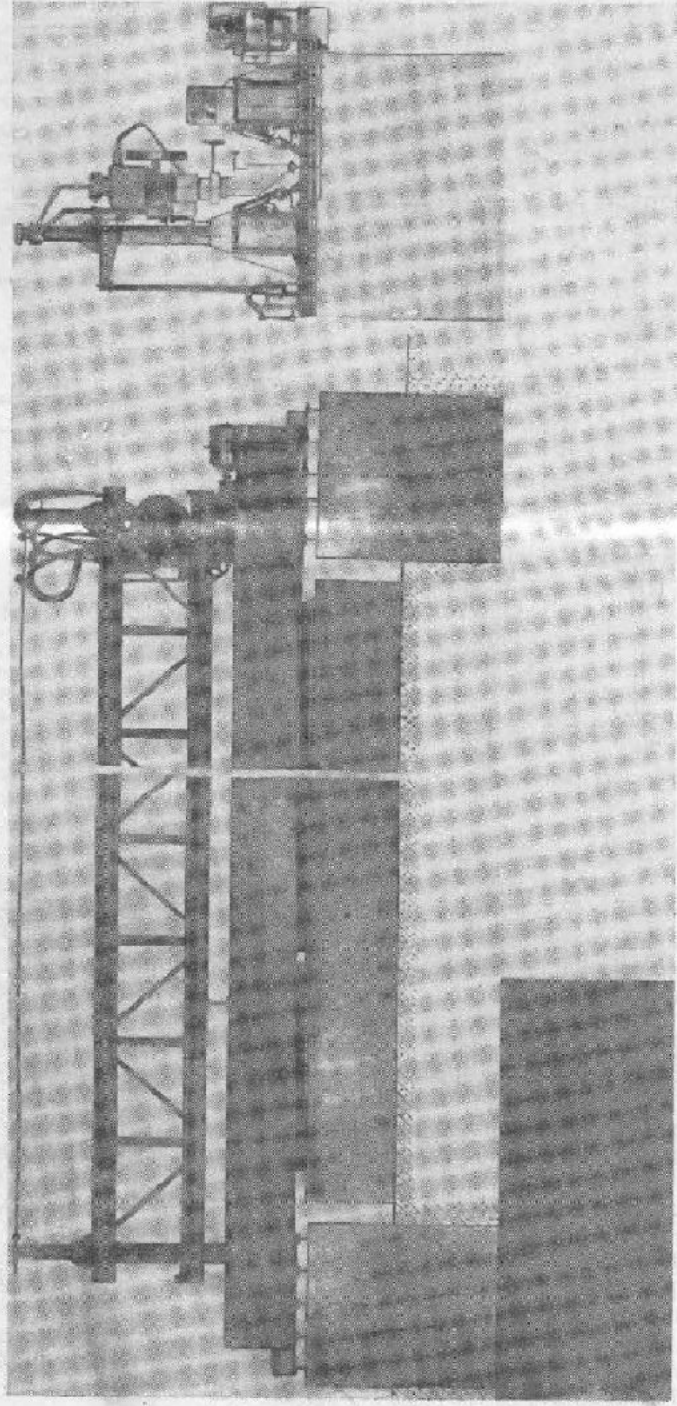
Самоходный агрегат со сварочными автоматами и гидравлическими прижимами для стыкуемых кромок.
